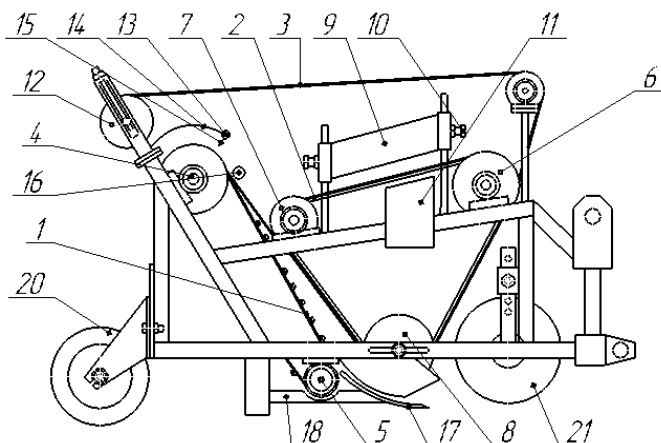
Схема модернизированного макетного образца картофелеуборочного комбайна с прутково-ленточным сепаратором
